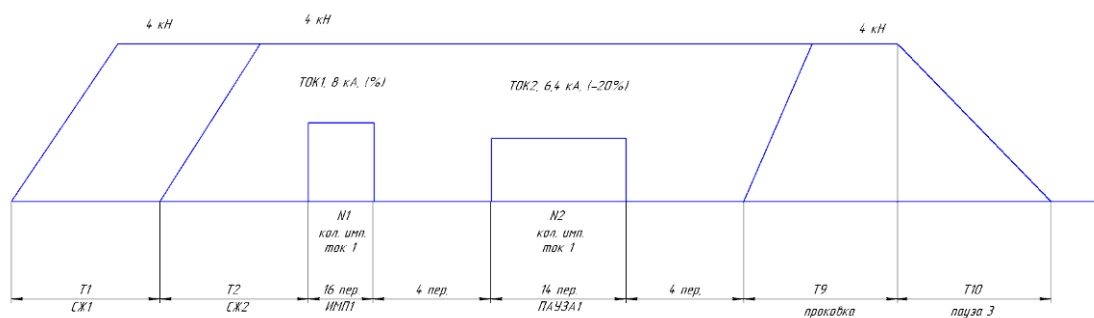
Циклограмма параметра режима контактной точечной сварки для определения величины сварочного диапазона
